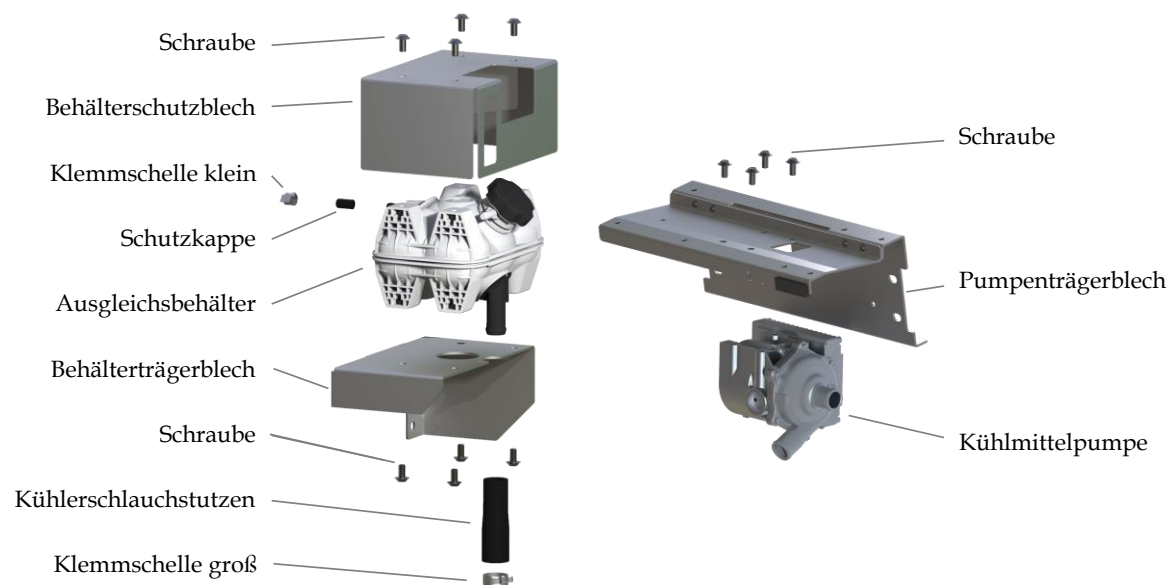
Unterbaugruppen Ausgleichsbehälter (links) und Kühlmittelpumpe (rechts)
